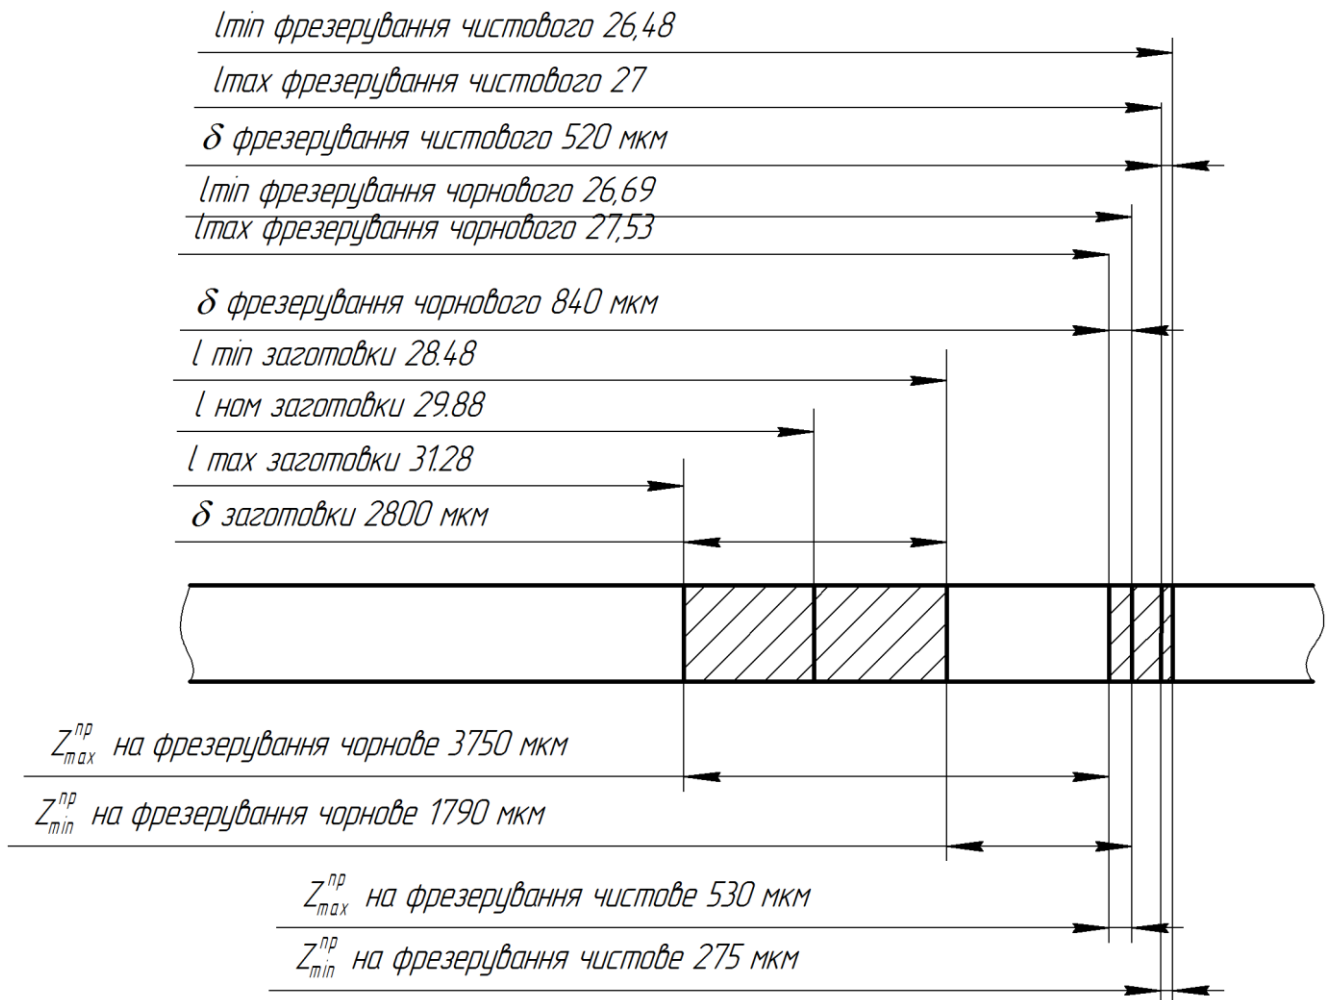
Схема графічного розташування припусків і допусків на обробку площини роз'єму "А" корпусу редуктора в розмір 27h14
